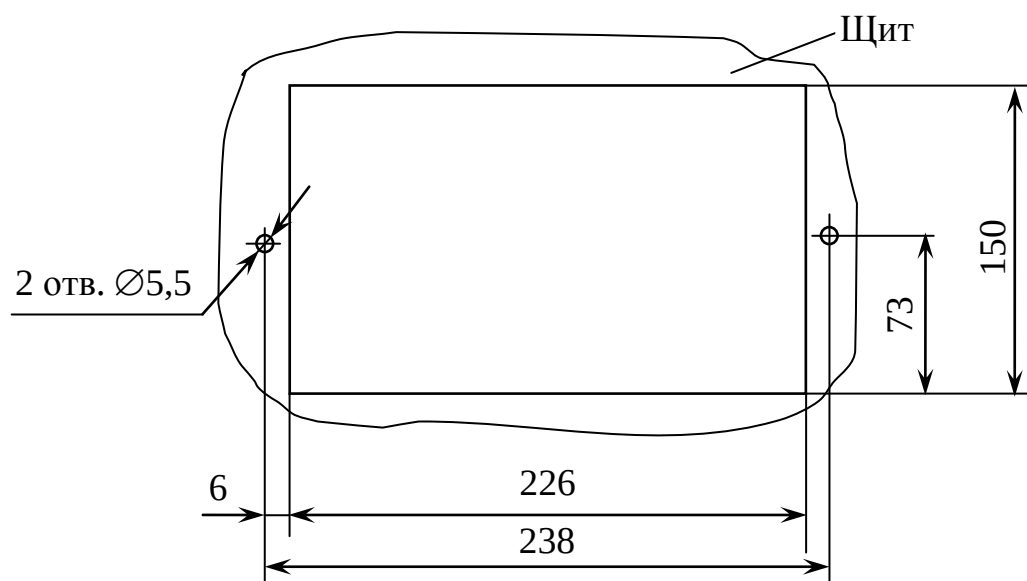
Разметка отверстий в щите для крепления блока преобразовательного щитового исполнения
